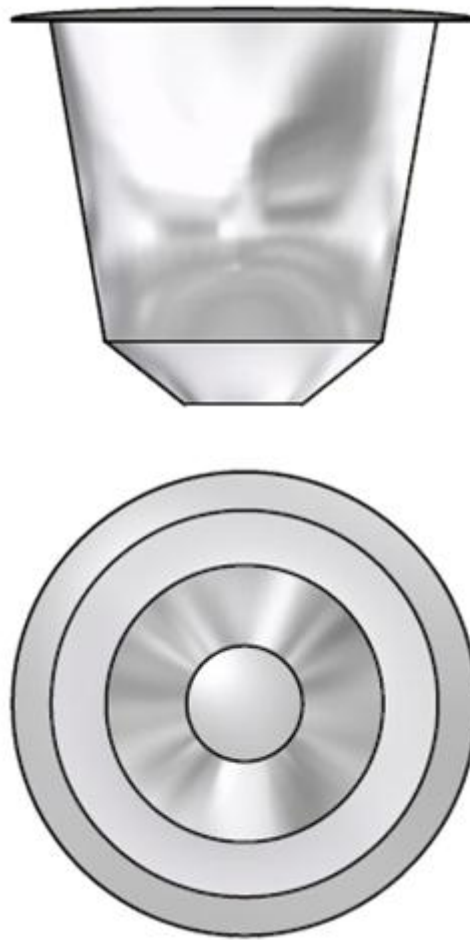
Alzado y planta de la cápsula actual de Nespresso. [NES12]
